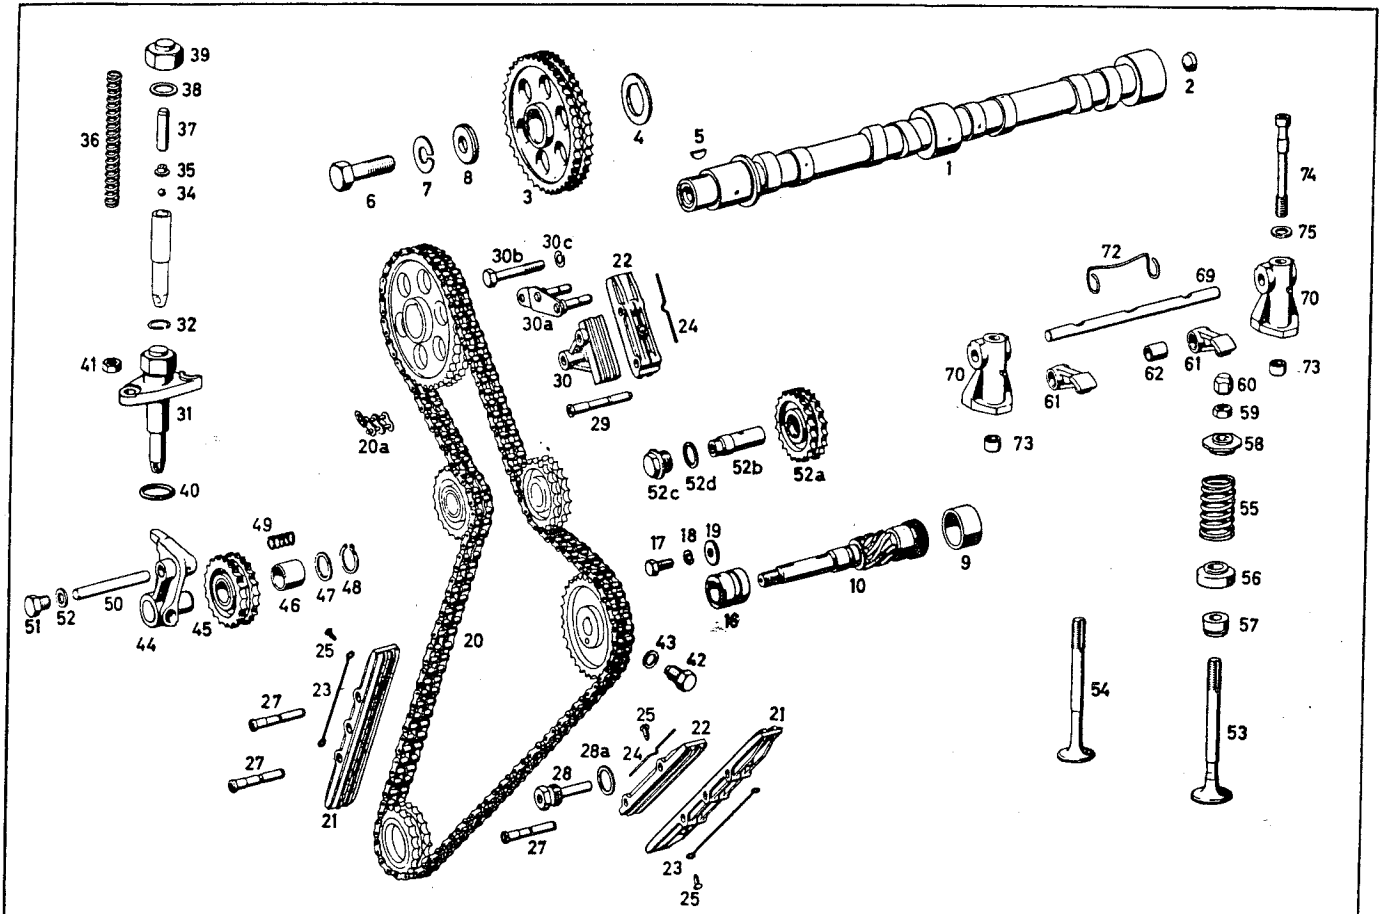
Montagebild der zerlegten Motorsteuerung (OM 621)
